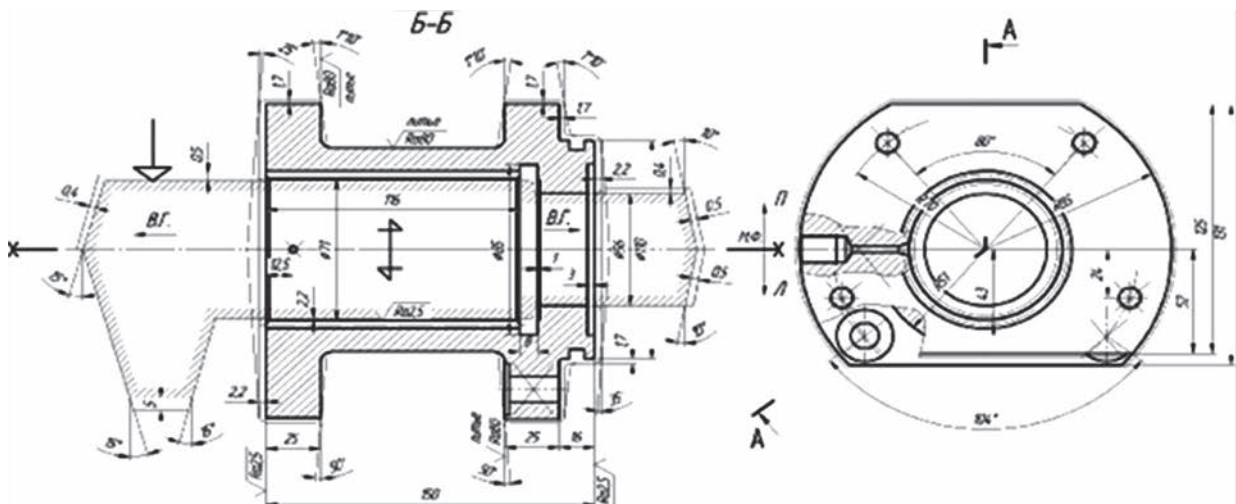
Чертеж детали «Корпус» с литейно-модельными указаниями
